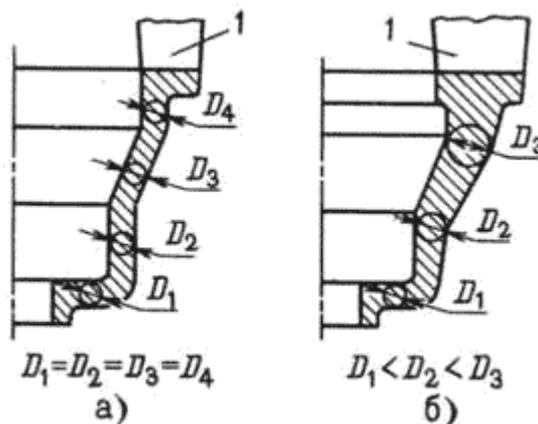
Конструкции литых деталей, обеспечивающих одновременное (а) и направленное (б) затвердевание отливок
